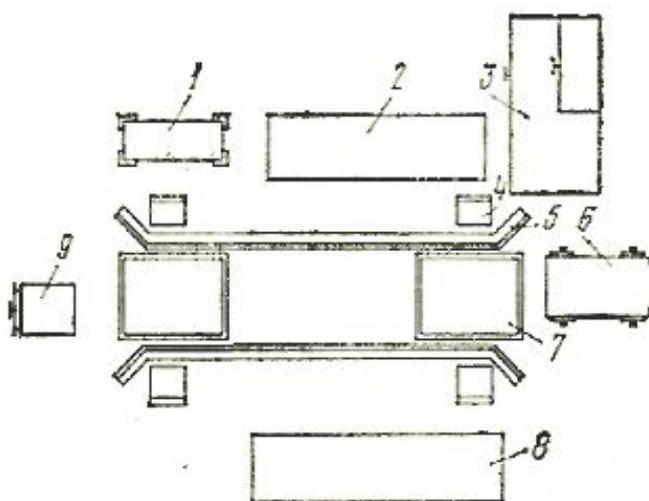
Схема рабочего гнезда на один стенд для ремонта ткацкого станка.
